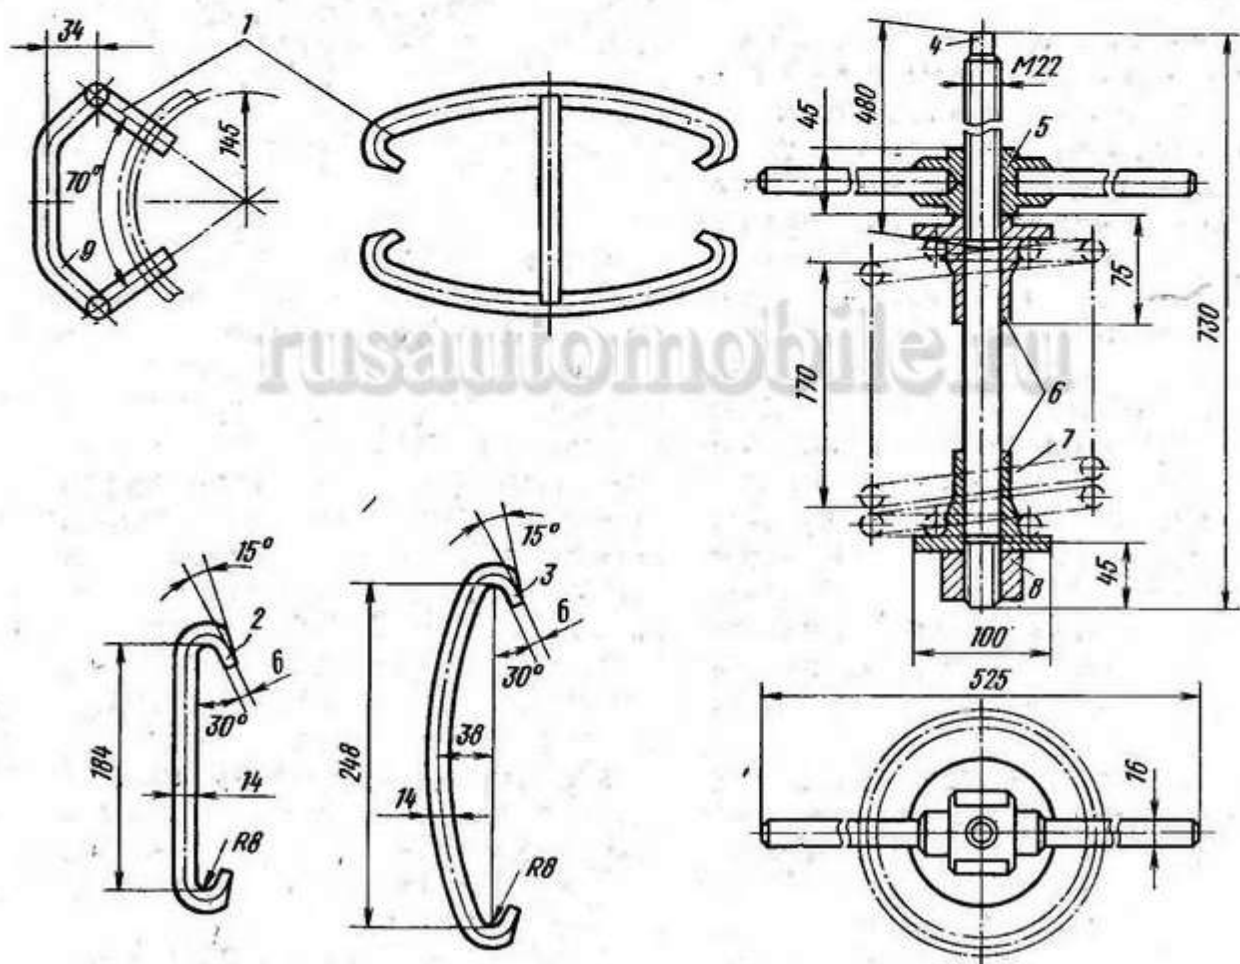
Приспособление для снятия и установки пружин откидывания:
